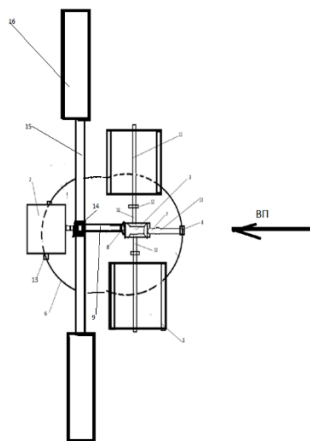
Оптимизированный ветродвигатель. Вид сверху
